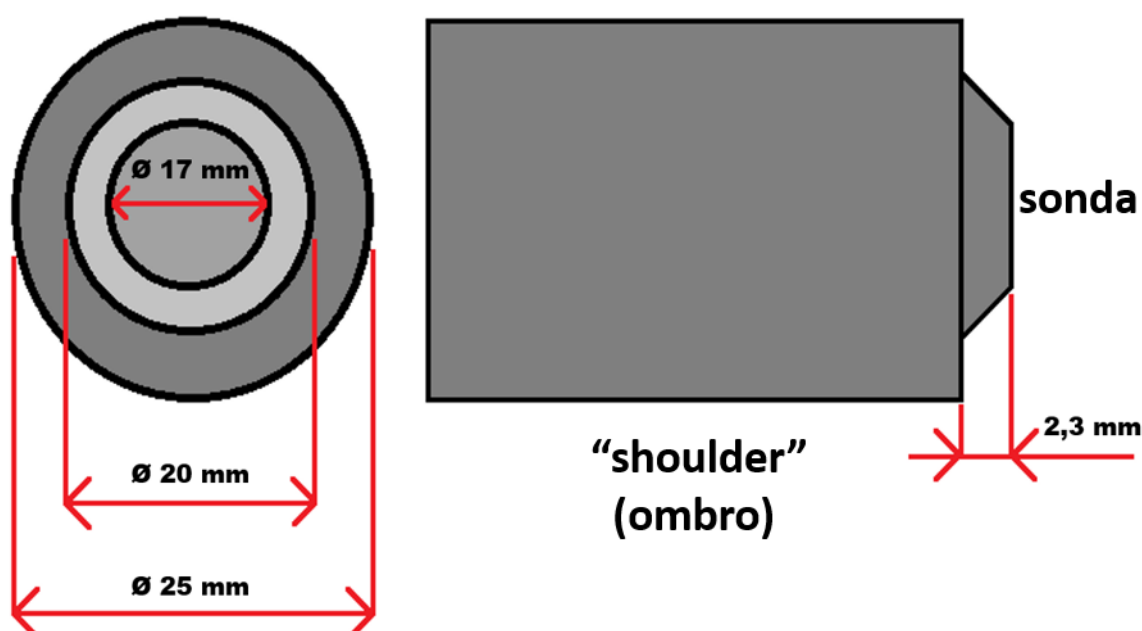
Dimensões da ferramenta de solda para um processo de soldagem por fricção linear (Fonte: próprio autor).
